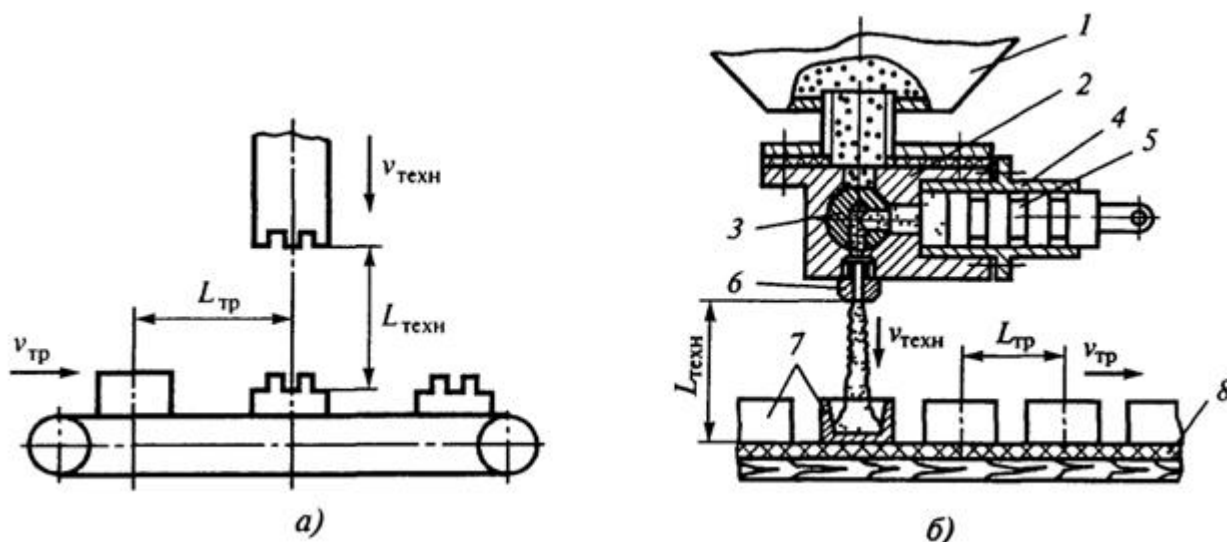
Операция I класса: *а* – схема операции; *б* – устройство для дозирования и формования массы в отливочной машине: 1 – бункер; 2 – корпус отливочной головки; 3 – золотник; 4 – мерный цилиндр; 5 – поршень; 6 – насадка; 7 – форма; 8 – ленточный конвейер
